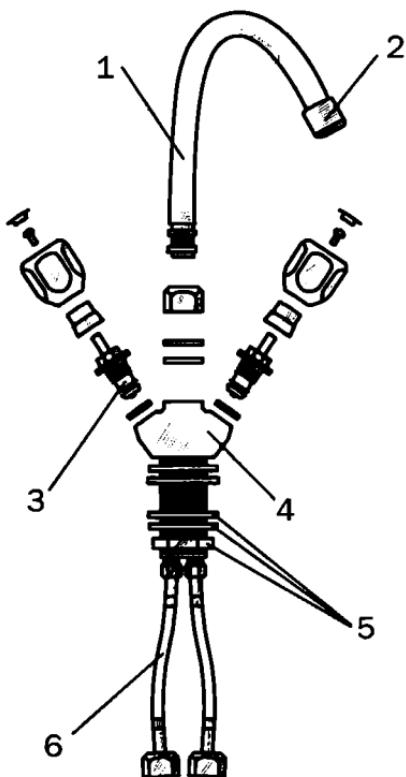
Конструкция двухвентильного смесителя типа «елочка»: 1 — излив; 2 — аэратор; 3 — вентильная головка; 4 — корпус; 5 — крепеж; 6 — подводка
